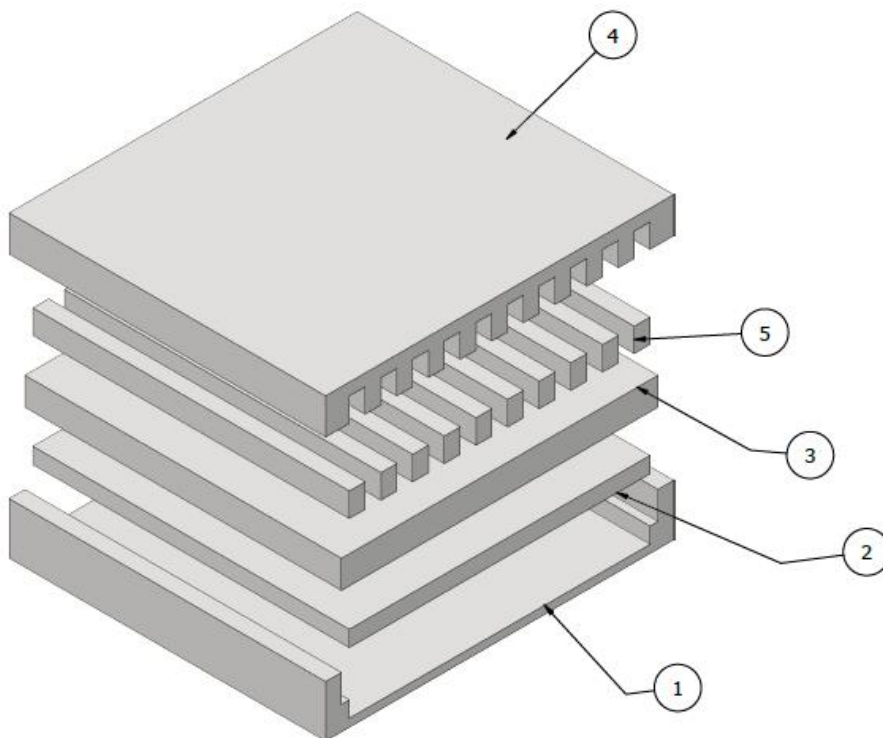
Diseño del modelo en CAD del evaporador capilar
